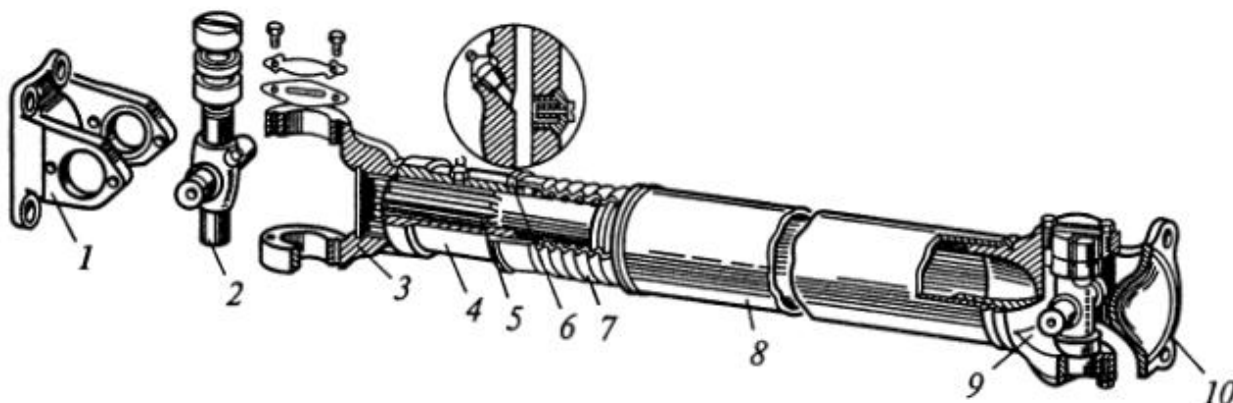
Карданная передача с шарниром неравных угловых скоростей: 1 – вилка; 2 – крестовина; 3 – скользящая вилка; 4 – втулка шлицевого соединения; 5 – шлицевой наконечник; 6 – манжета; 7 – чехол; 8 – труба вала; 9 – вилка; 10 – вилка
